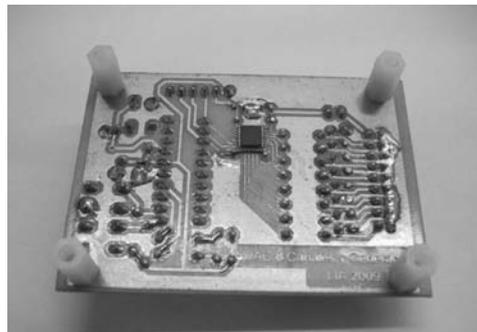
Imagen del lado soldadura del prototipo.
